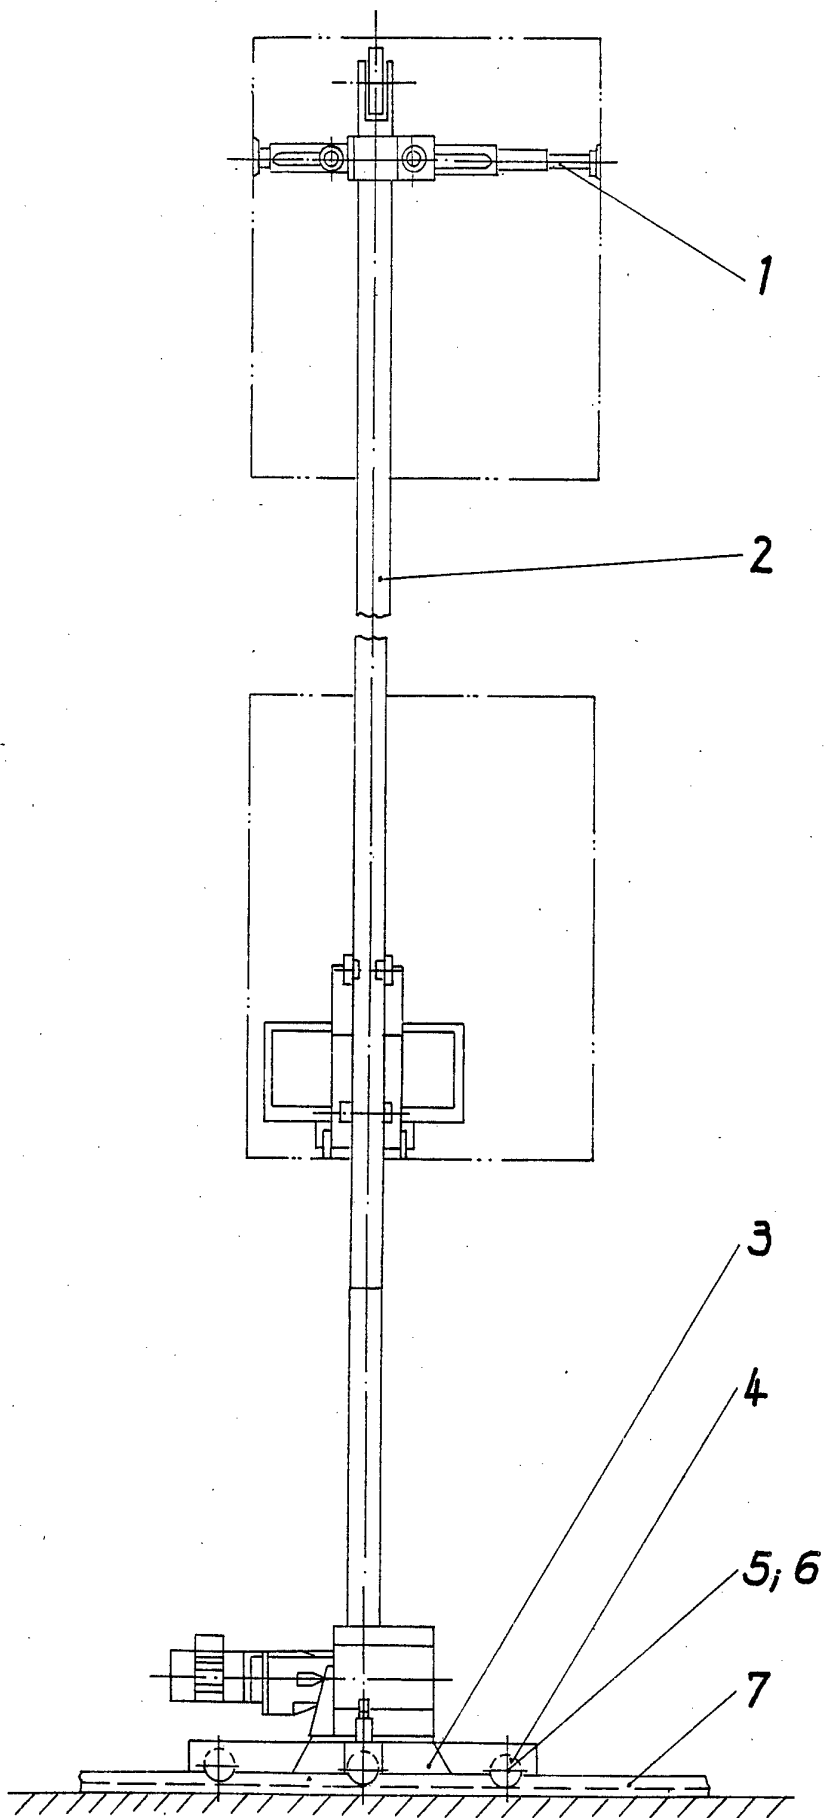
Einständertragwerk eines Kleinbauaufzuges mit Dreiradlagerung; Vorderansicht
